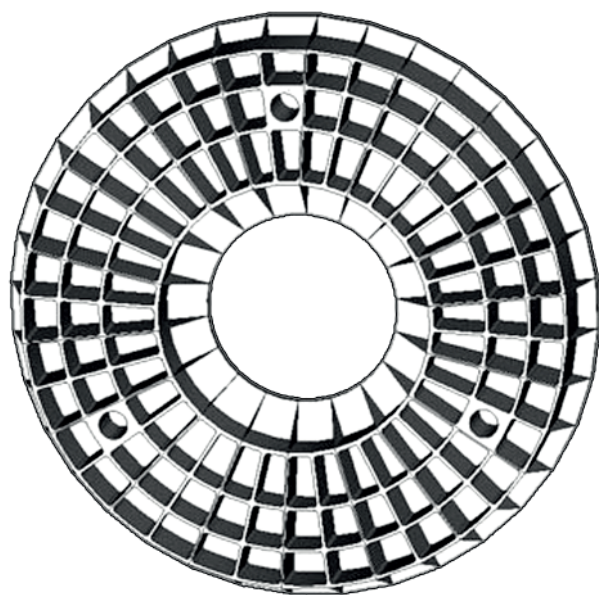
Конструкция зеркала из ситалла СО-115М.
